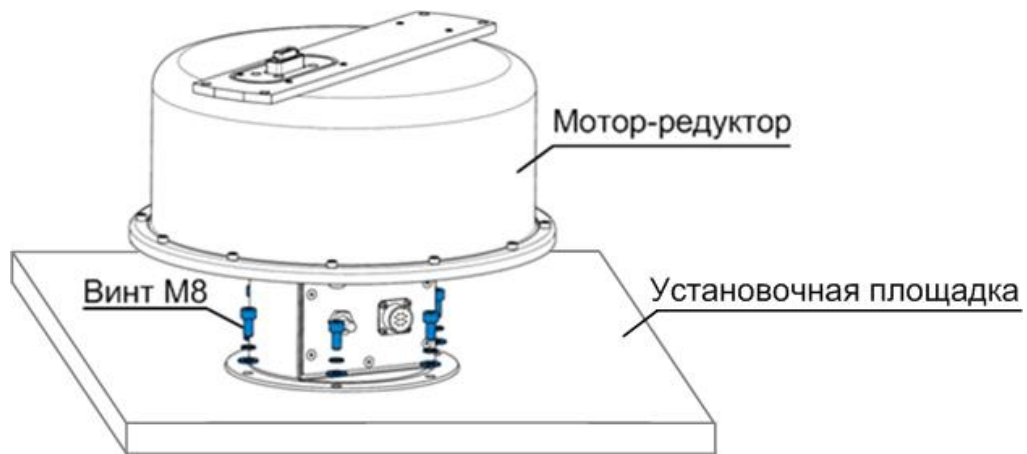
Крепление мотор-редуктора к установочной площадке
